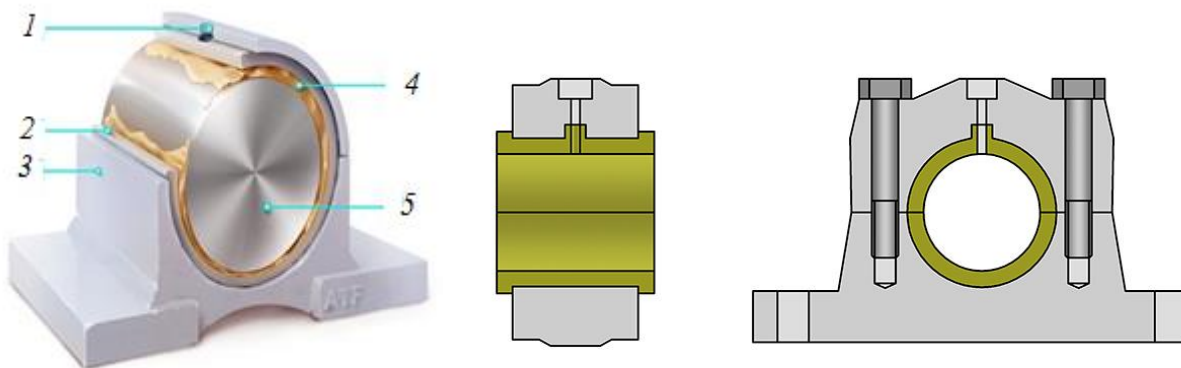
Підшипник ковзання: 1– кришка; 2 – вкладиш; 3 – корпус; 4 – мастило; 5 – вал
